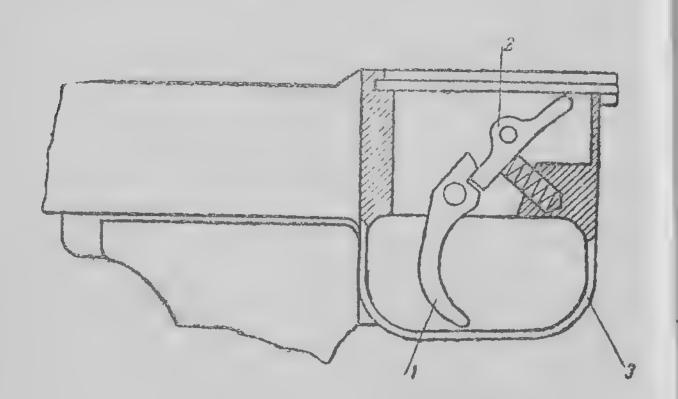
Спусковой механизм: 1 спусковой крючок; 2—спусковой рычаг с пружиной; 3—предохранительная скоба
